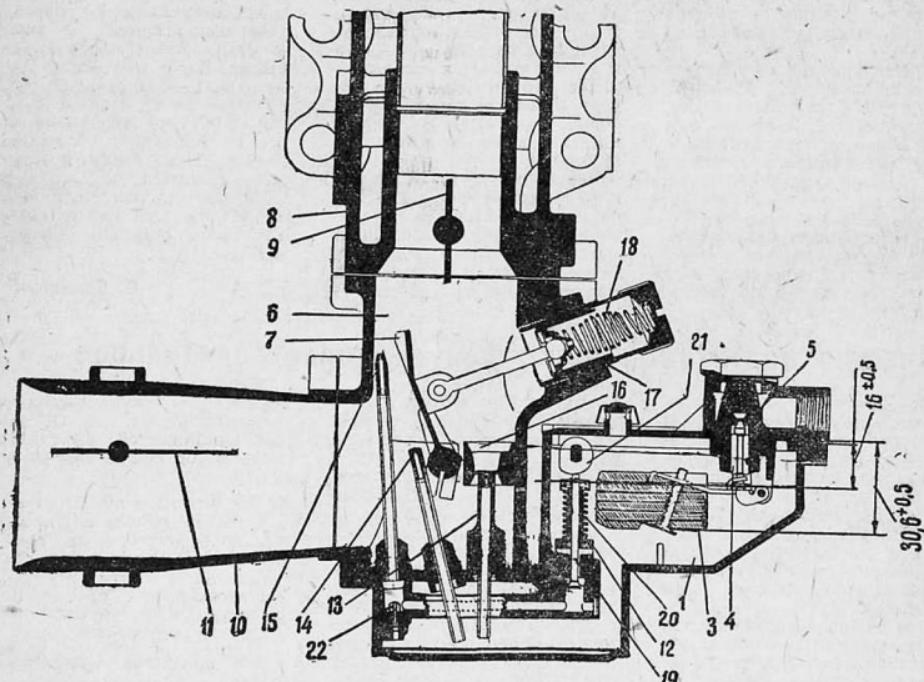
Схема карбюратора легкового автомобиля ЗИС: 1—поплавковая камера; 3—поплавок; 4—запорная игла; 5—фильтр; 6—корпус смесительной камеры; 7—автоматическая заслонка; 8—подогреватель; 9—дроссельная заслонка;
